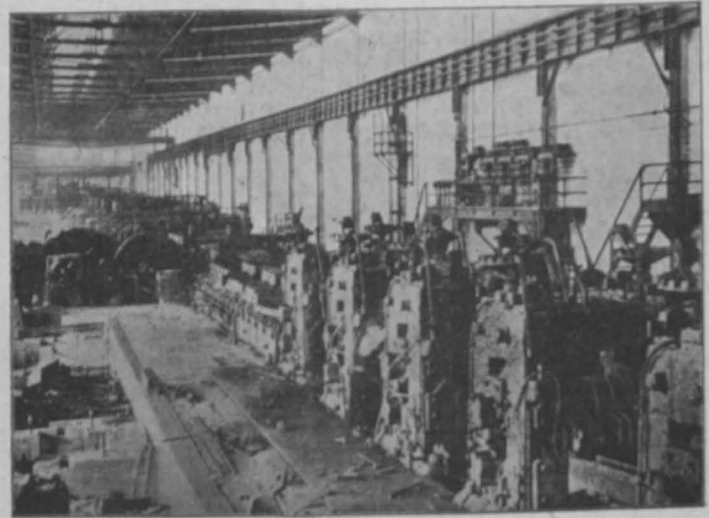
Größtes kontinuierliches Knüppel-Walzwerk der Welt; United Engineering & Foundry Company, Pittsburg
